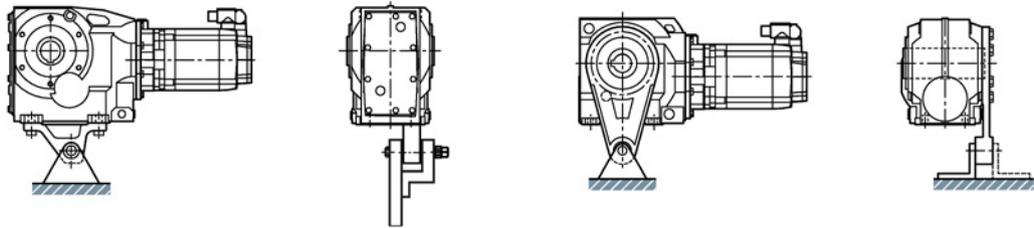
Montagevorschlag für Drehmomentstütze an Fuß und Flansch
